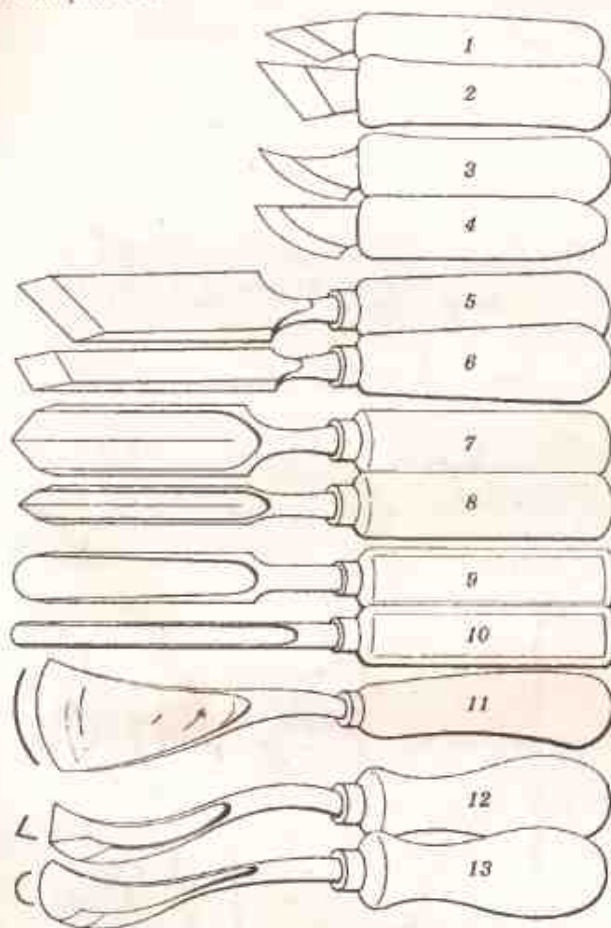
Основные инструменты для контурной резьбы: 1, 2 — ножи-косяки; 3, 4 — ножи-резаки; 5, 6 — стамески-косяки; 7, 8 — стамески-уголки; 9, 10 — полукруглые стамески; 11 — отлогая стамеска; 12 — клюкарза-уголок; 13 — клюкарза полукруглая
